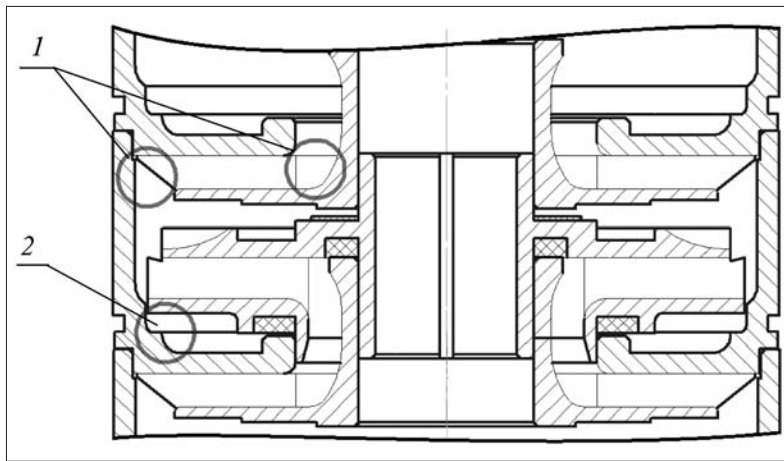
Части проточного канала ступени, наиболее подверженные гидроабразивному разрушению:
